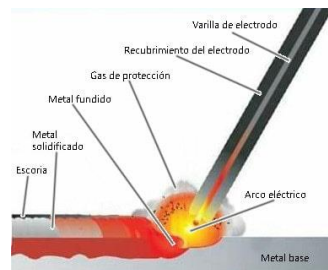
Proceso de soldadura SMAW [21]
